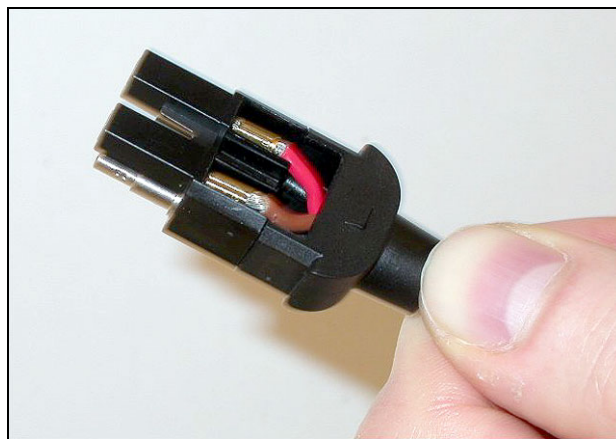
Montage von Block und hinterem Gehäuse
